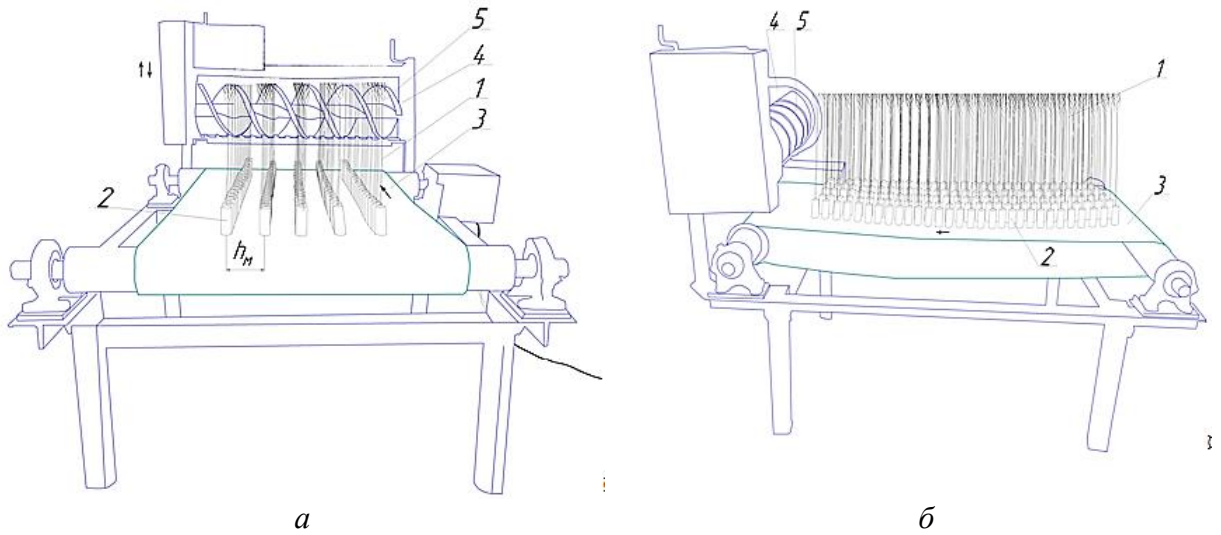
Схема опытного лабораторного образца со стеблями:
